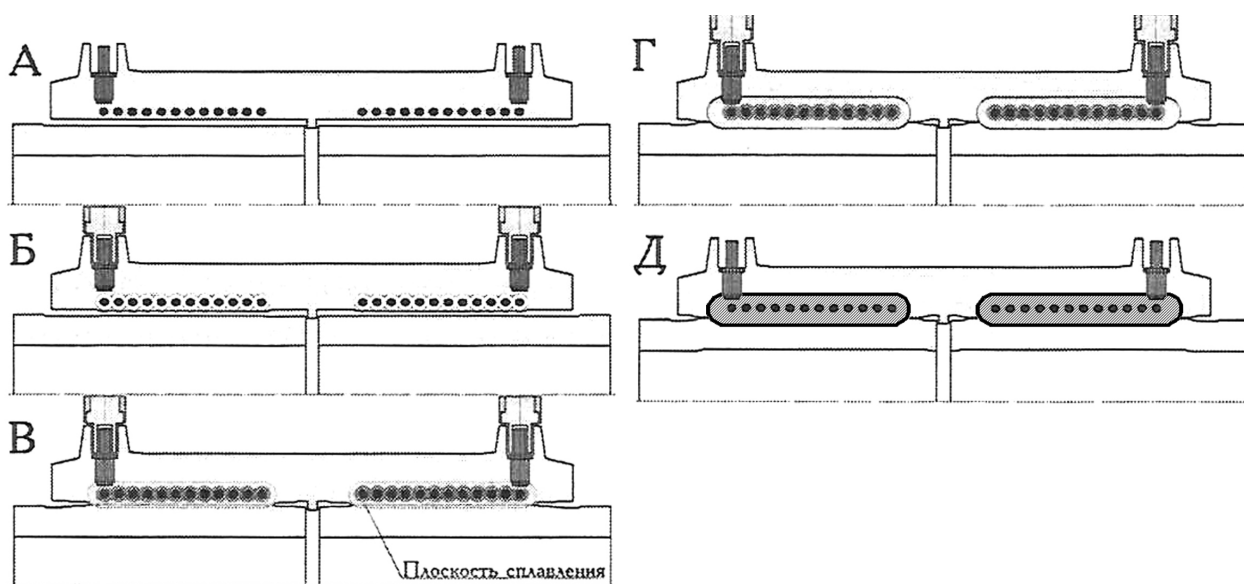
Последовательность этапов формирования шва при сварке труб деталями с ЗН:
